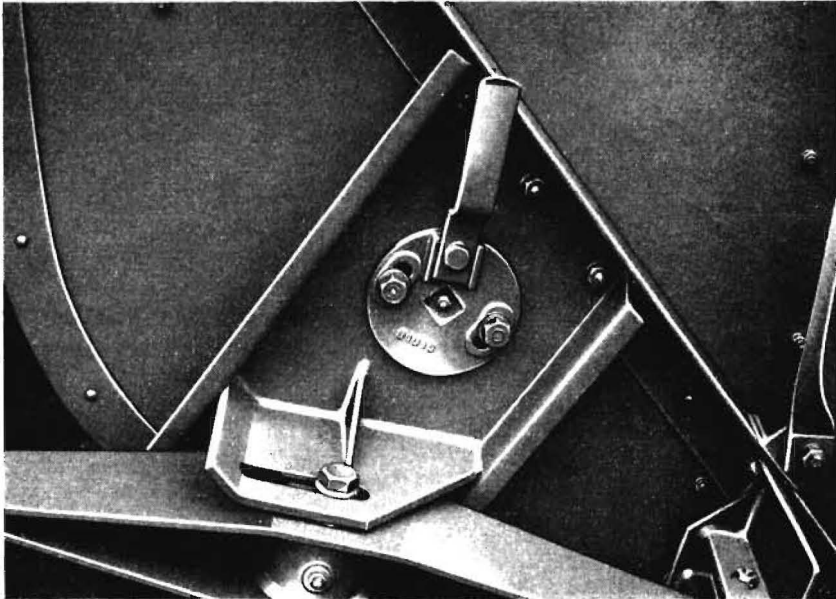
Einstellhebel für die Exzenterwelle der Förderschnecke
